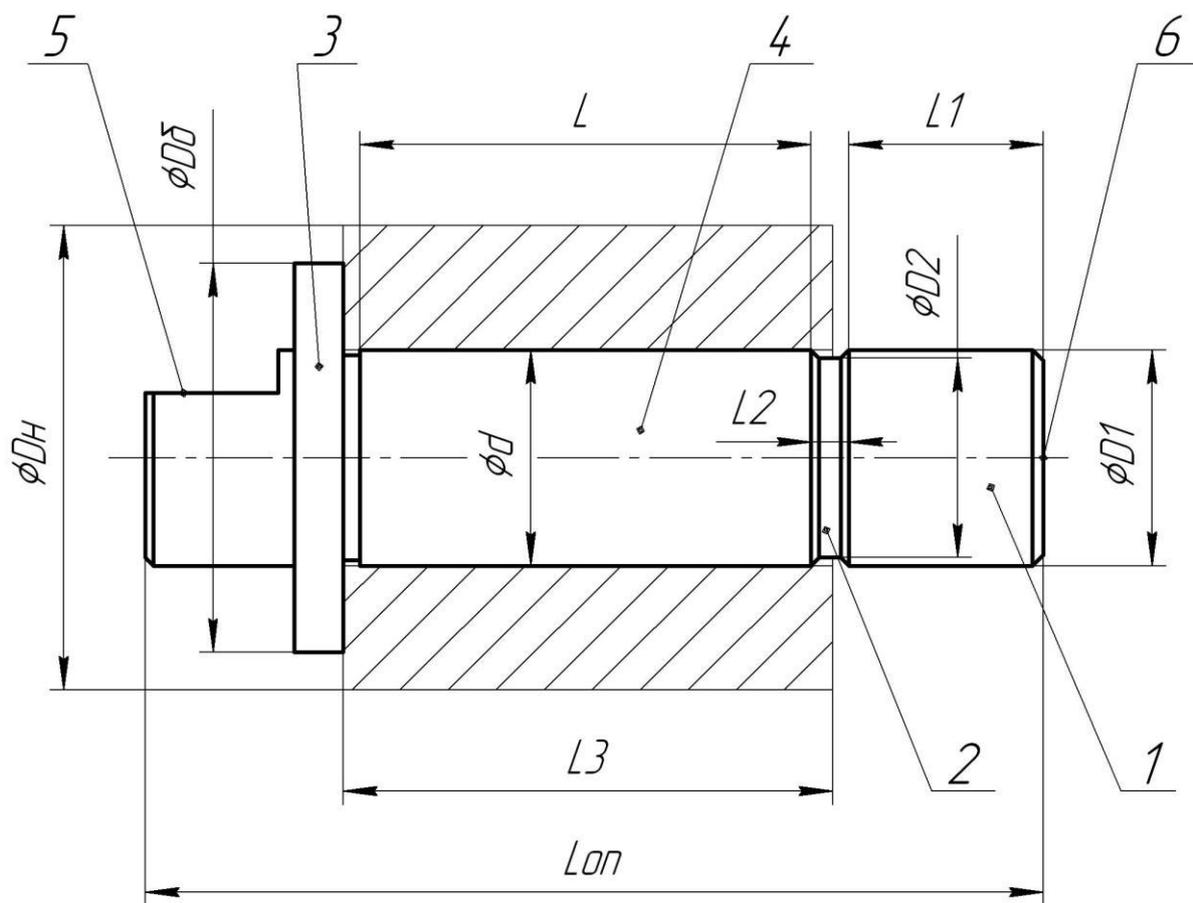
Цилиндрическая оправка для посадки заготовок с натягом
